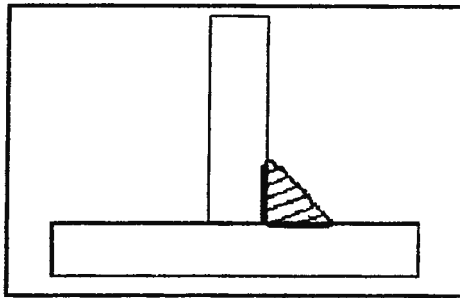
Forma ideal de soldadura de filete
